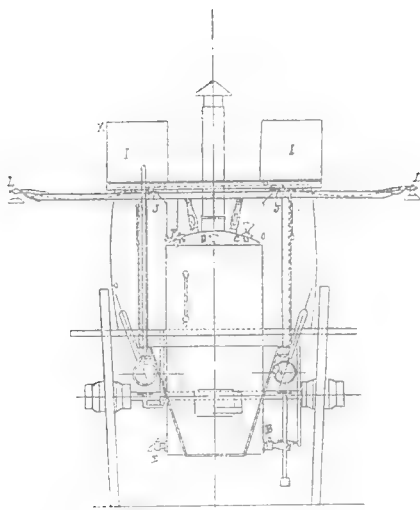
Voiture à désinfection et douches. — Coupe en travers.
